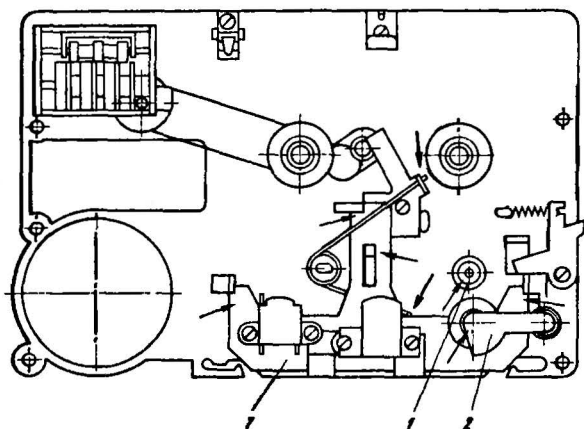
Внешний вид ЛПМ (вид сверху). Места смазки ЛПМ (→)
